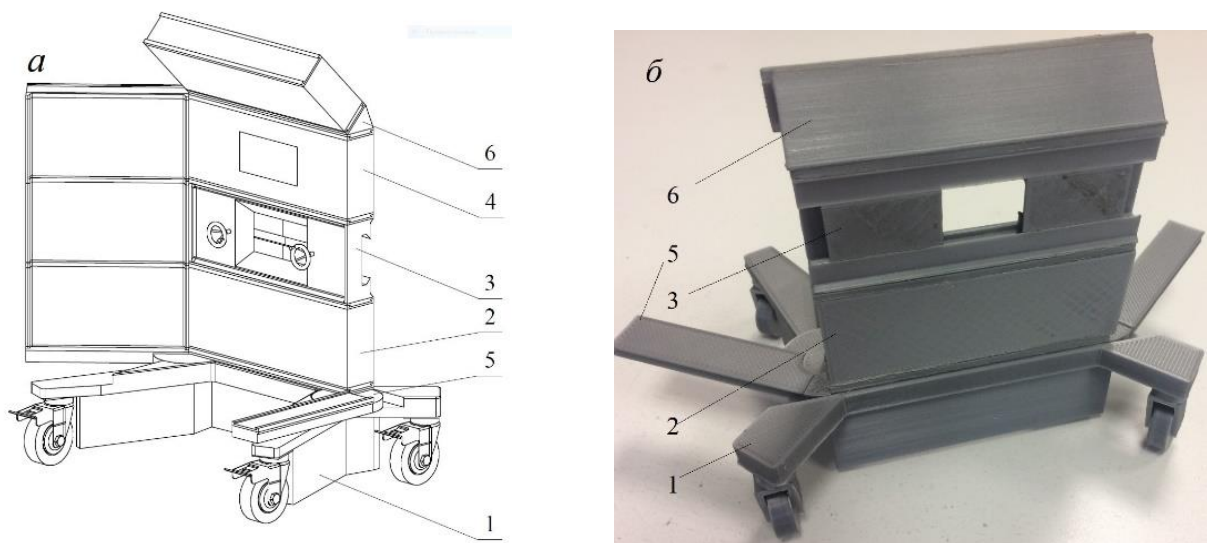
Чертеж (а) и модель, изготовленная на 3D-принтере (б) сборной мобильной биологической защиты: 1 – основание; 2 – основные блоки; 3 – блок с защитными шторками; 4 – блок с защитным стеклом; 5 – поворотные консоли для боковой защиты; 6 – переходные элементы
